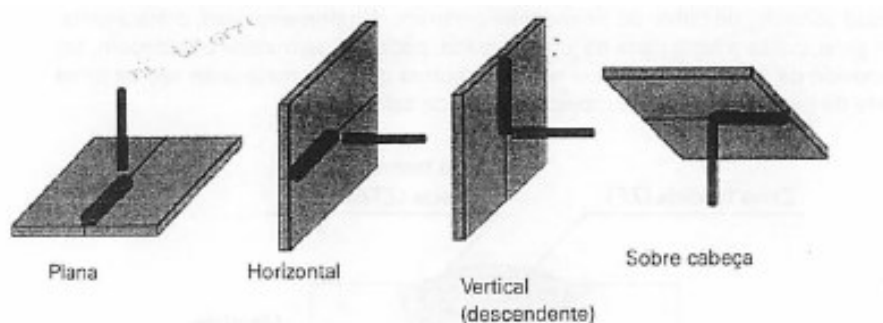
Posição de solda de topo. (MARQUES et al., 2011).
